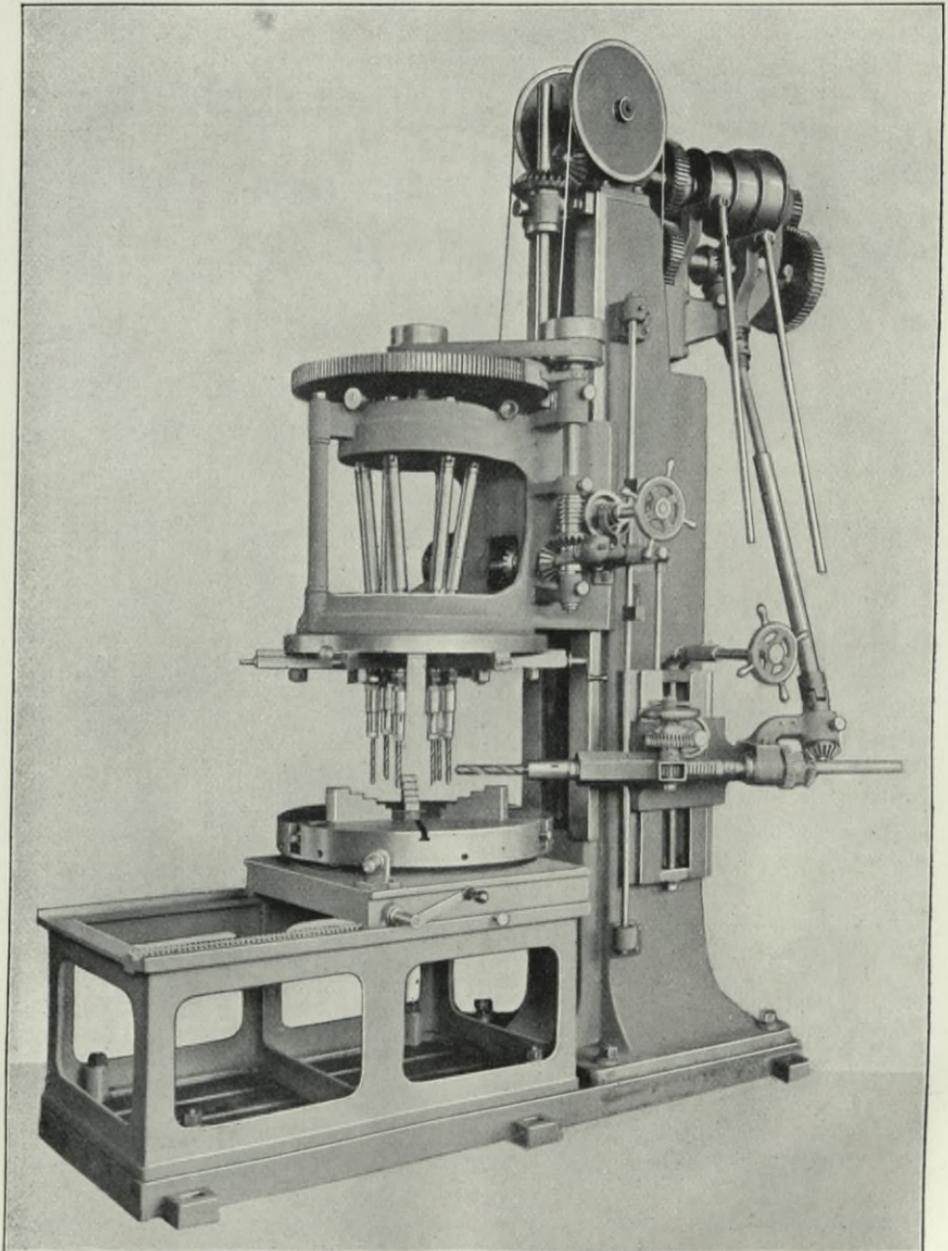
Düsseldorfer Werkzeugmaschinenfabrik Habersang & Zinzen.
